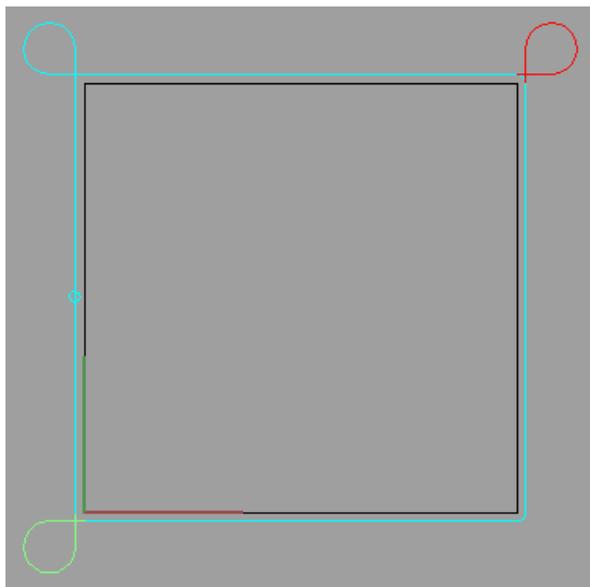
Схема обработки заготовки с помощью инструмента «Петля» в ручном режиме
